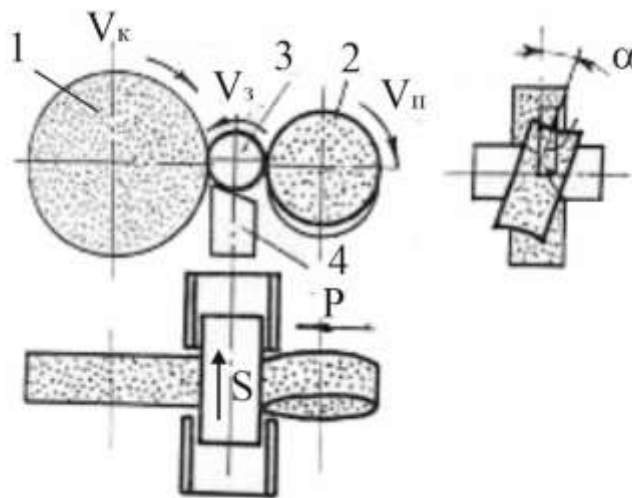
Схема безцентрового шліфування: 1 – шліфувальне коло; 2 – коло, що подає; 3 – заготовка; 4 - підтримуючий (опорний) ніж.
